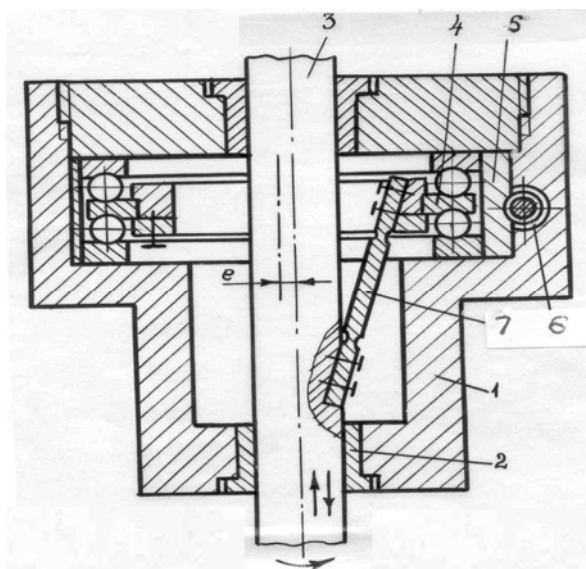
Механізм перетворення обертового руху в осьові коливання вала
